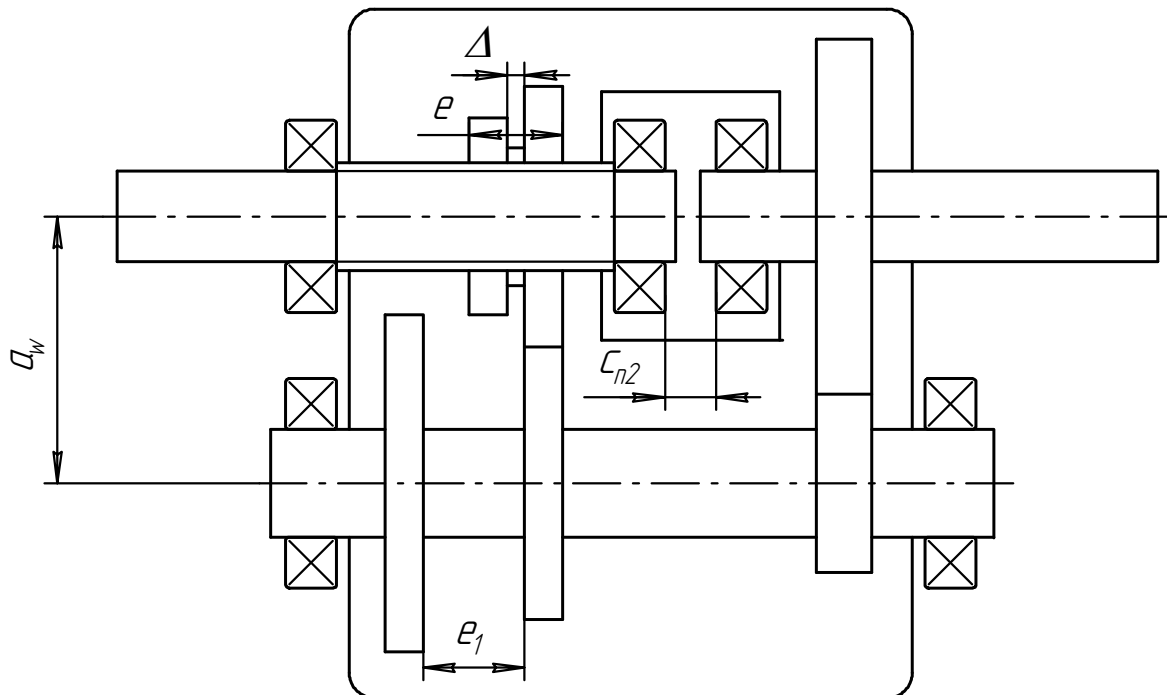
Расположение колёс и подшипников соосного цилиндрического редуктора
